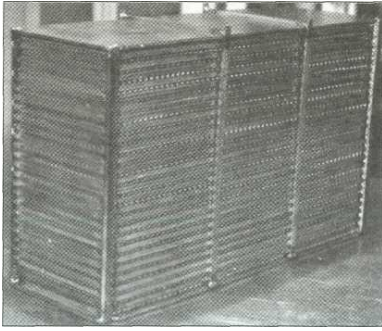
Сталевий ПРЕ, підготовлений до паяння
